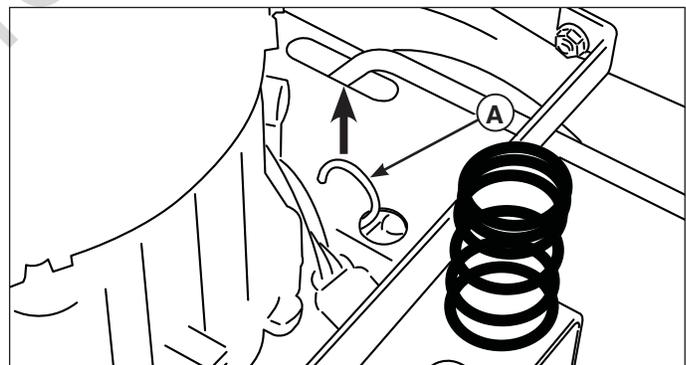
Componentes de liberación de rodamiento (en cada lado)
